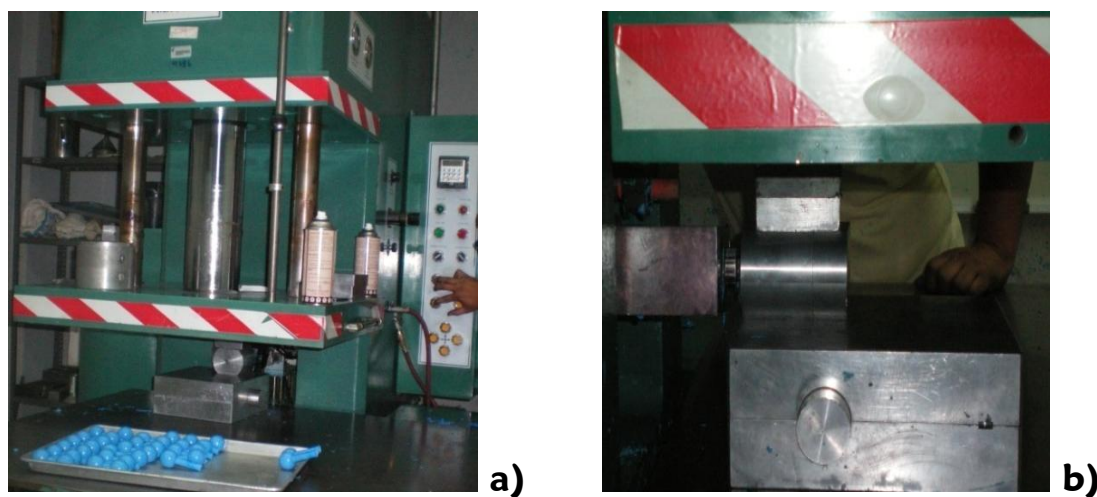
a) Máquina de inyección y, b) inyección de cera al molde.
